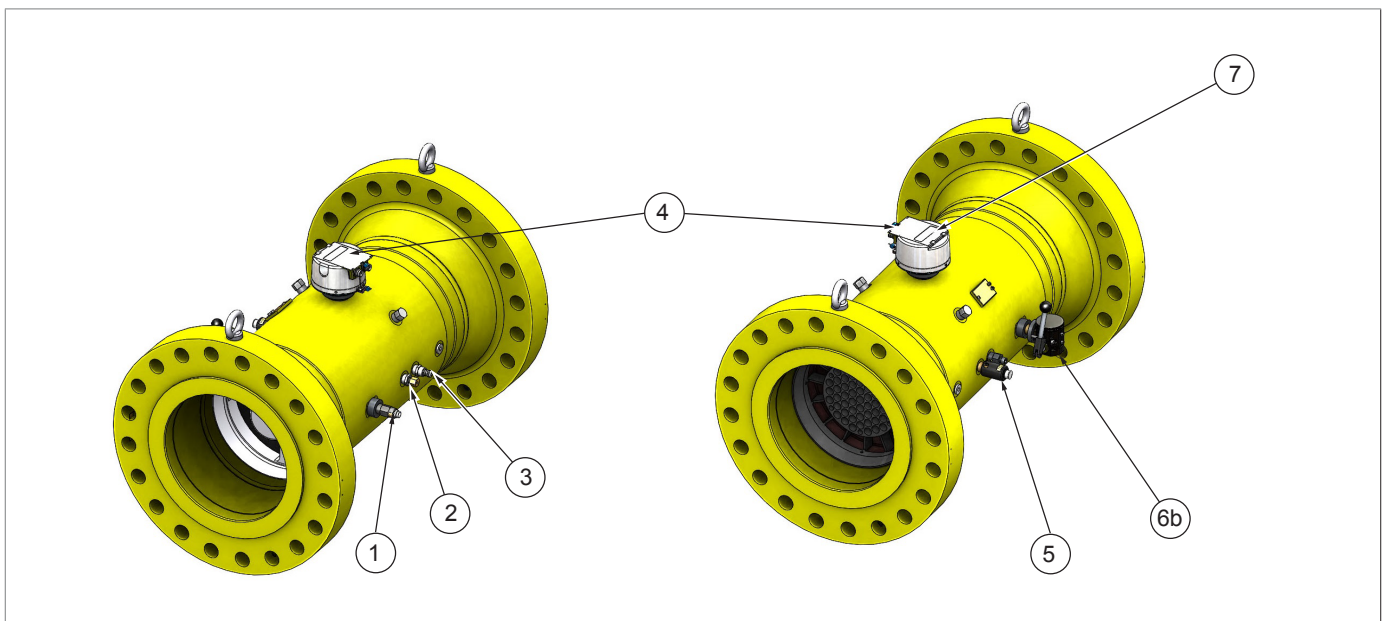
Posicionamiento de conexiones y accesorios del contador iM-TM cuerpo de acero
